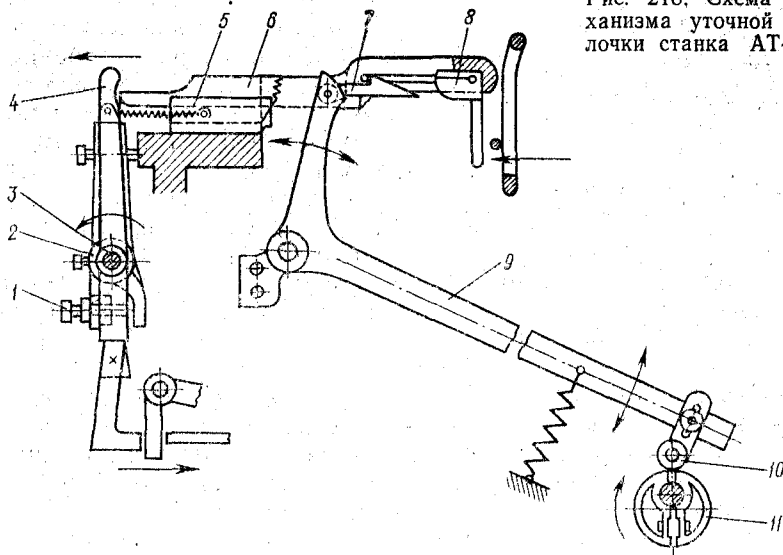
Схема механизма уточной вилочки станка АТ-100
